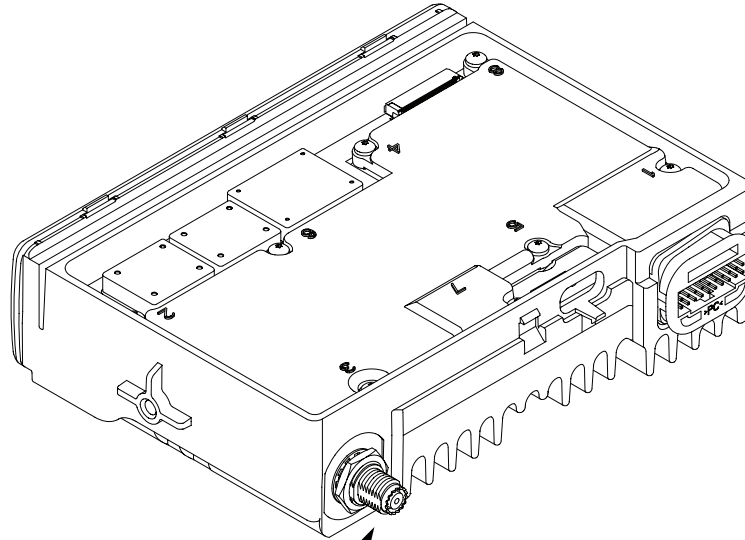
Basınçlı Döküm Ana Kaplamasının Gövdeye Takılması
